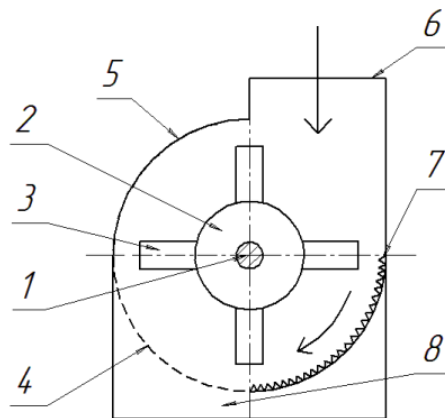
Загальна схема молоткової дробарки: 1 – вал; 2 – молотковий ротор; 3 – молоток; 4 – решето; 5 – корпус; 6 – завантажувальний патрубок; 7 – дека; 8 – відвідний патрубок.
